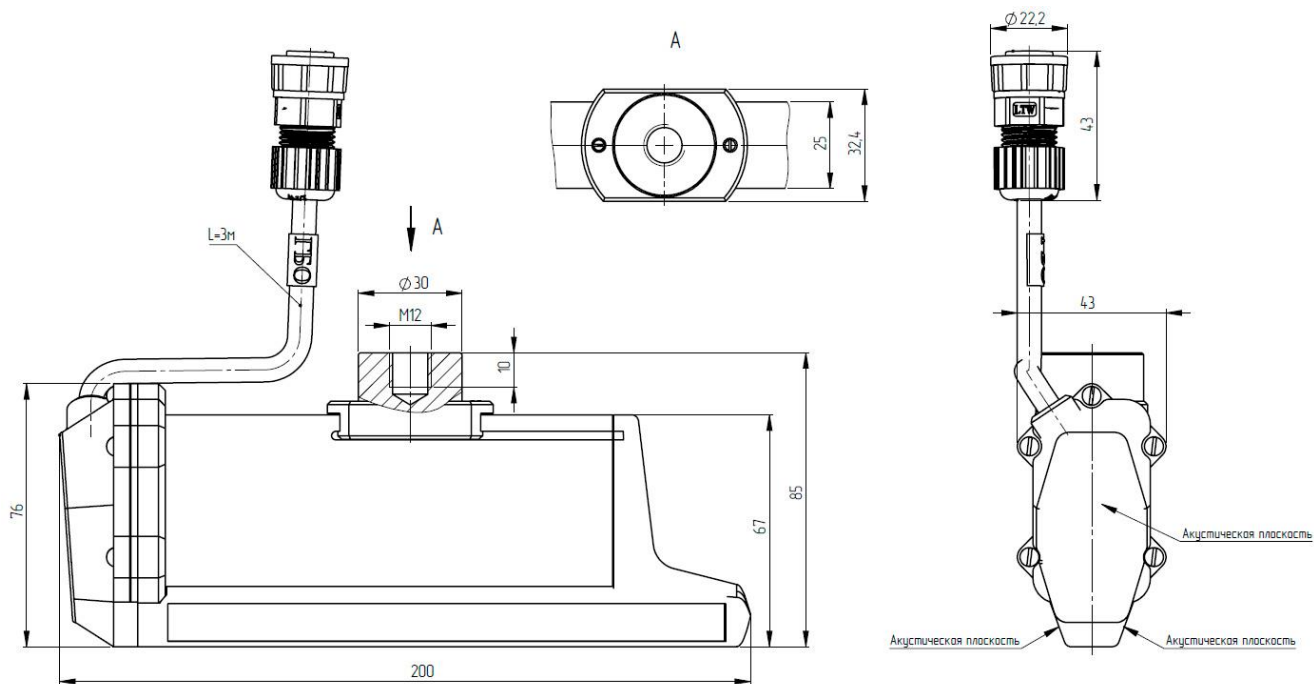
Габаритный чертеж моноблока (кронштейн для крепления к штанге из набора КИТ006)
